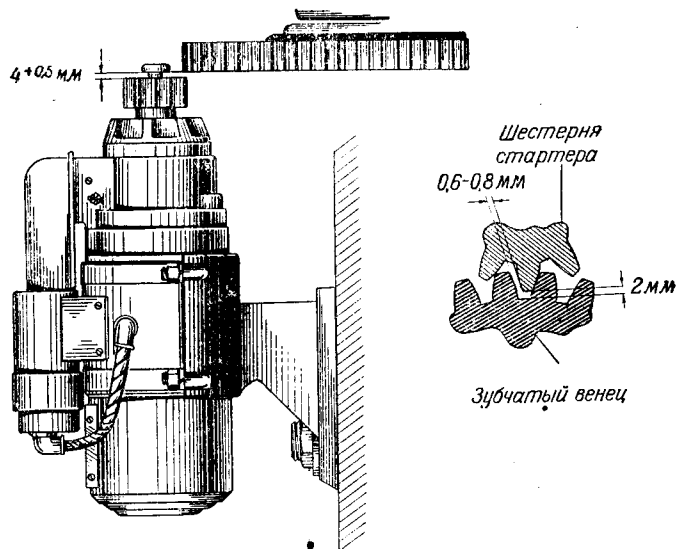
Установочные зазоры между шестерней стартера и зубчатым венцом первичного привода вентиляторов
